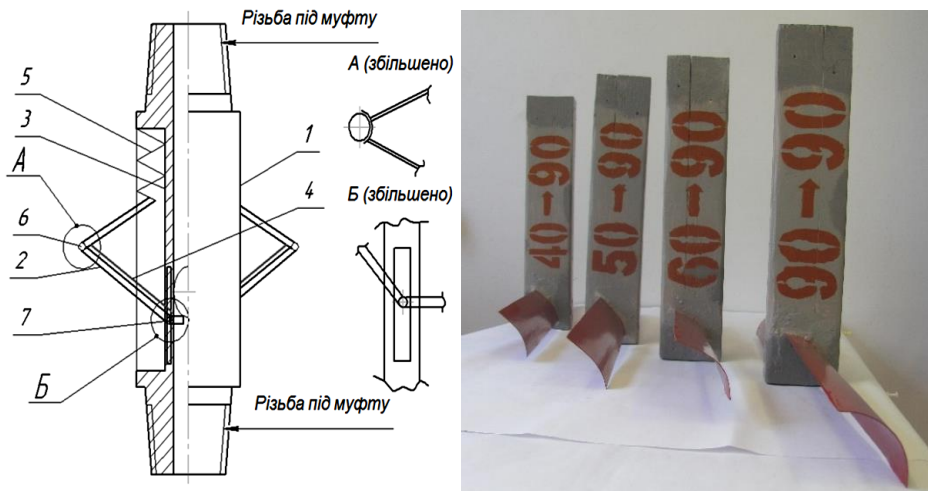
Принципова схема пристрою для обробки стовбура свердловини та робочі моделі його лопатевого робочого органу
